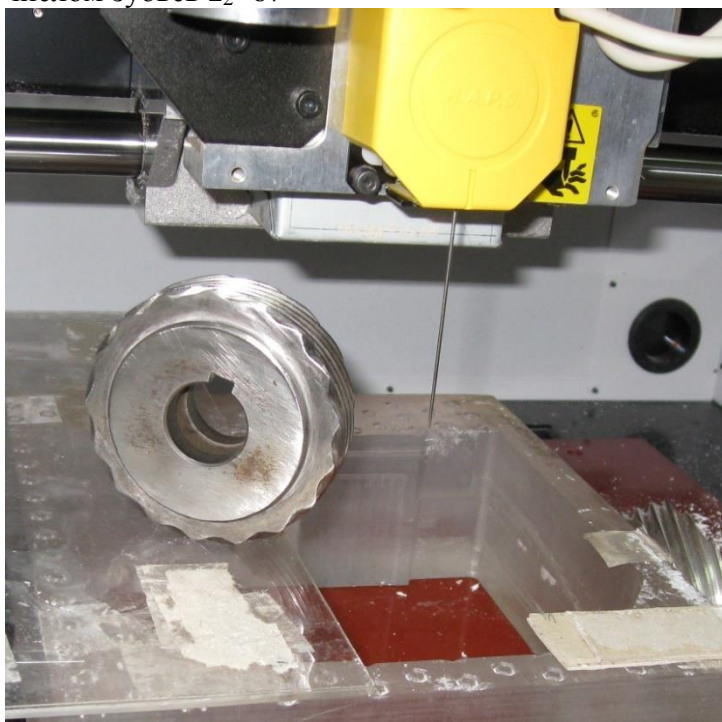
Схема контроля профиля накатанного зуба и его погрешность
